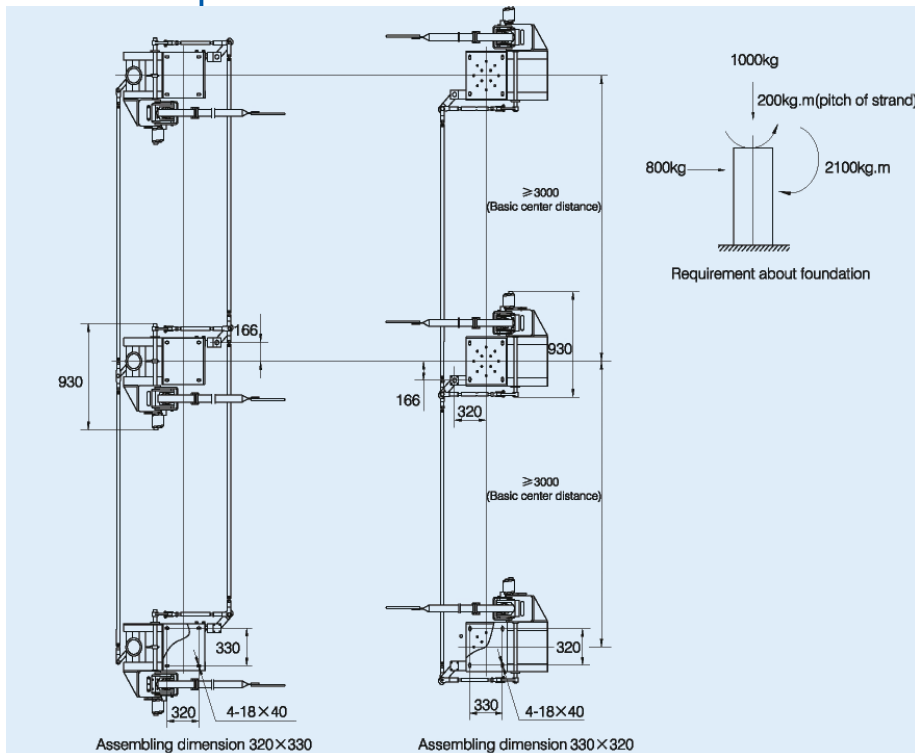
Внешний вид и размеры разъединителя GW23-252
